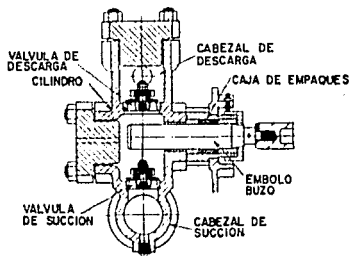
EXTREMO DEL LIQUIDO DE UNA BOMBA RECIPROCANTE HORIZONTAL .
